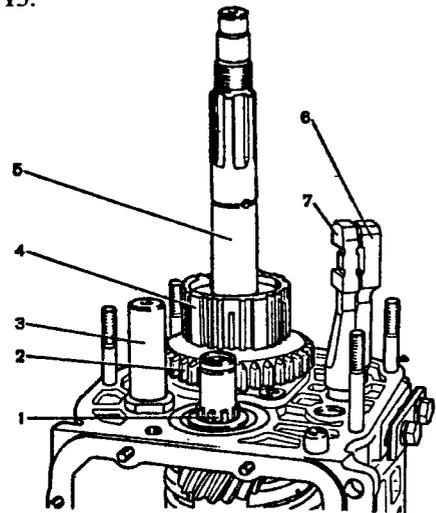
Снятие ведомой шестерни заднего хода и ступицы муфты синхронизатора V передачи: 1 - промежуточный вал; 2 - ведомая шестерня заднего хода; 3 - ось промежуточной шестерни заднего хода; 4 - ступица муфты синхронизатора V передачи; 5 - вторичный вал; 6 - шток вилки включения I и II передач; 7 - шток вилки включения III и IV передач
